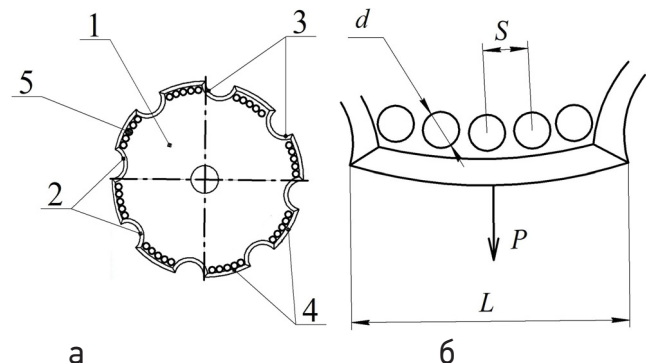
Схемы: а – вырезного диска с наплавкой; б – размещения элементов прерывистой твердосплавной наплавки
